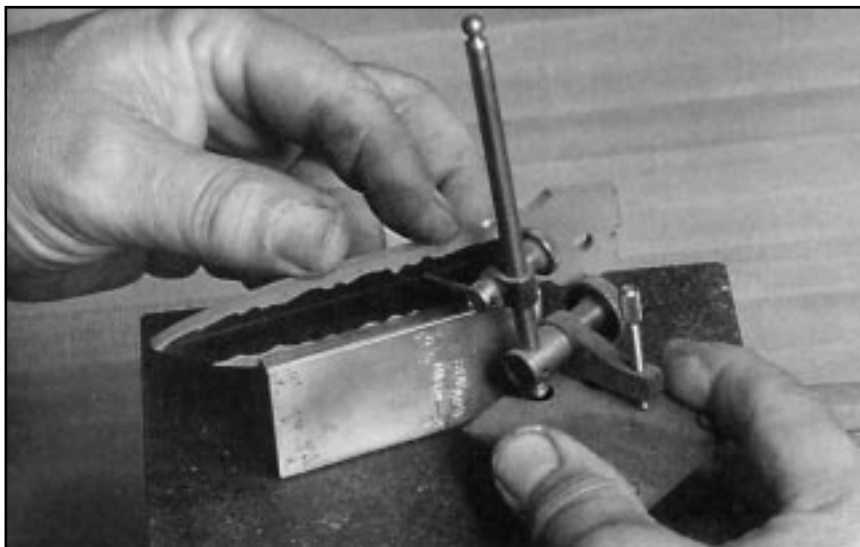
Разметьте линии спусков на обеих сторонах клинка перед шлифовкой. Я устанавливаю клинок вертикально в паз штатива и фиксирую клинок режущей кромкой вниз.
